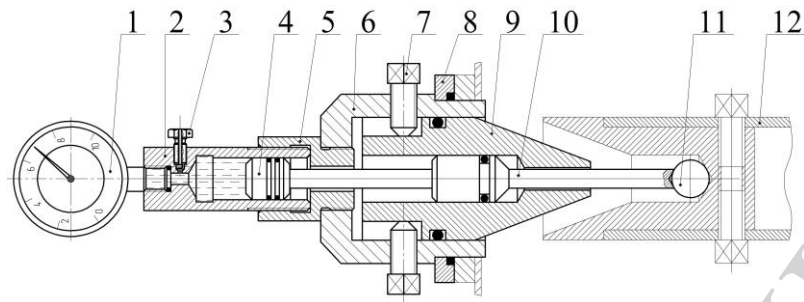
Конструктивна схема пристосування: для визначення осьового навантаження: 1 – манометр; 2 – гільза; 3 – штуцер; 4 – поршень; 5 – втулка різьбова; 6 – корпус; 7 – регулювальні гвинти; 8 – фланець; 9 – цапфа; 10 – плунжер; 11 – кулька; 12 – шнековий вал
